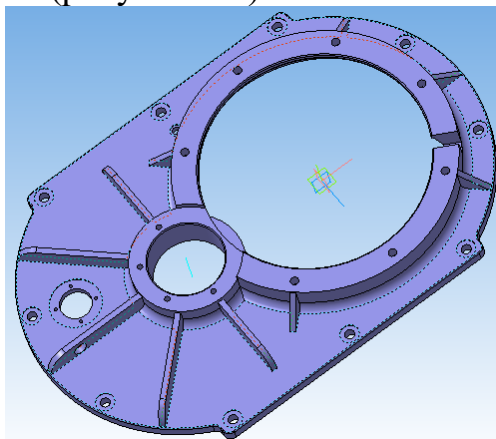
Тривимірне креслення заготовки і деталі
